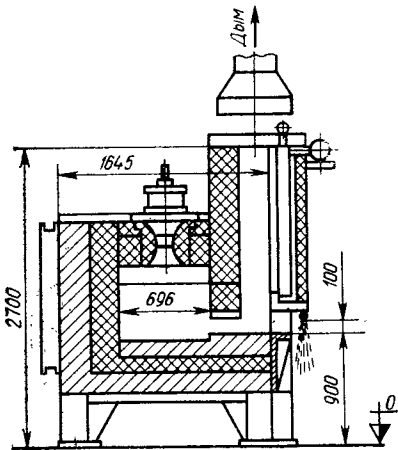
Камерная щелевая нагревательная печь с обогревом плоскопламенной горелкой
